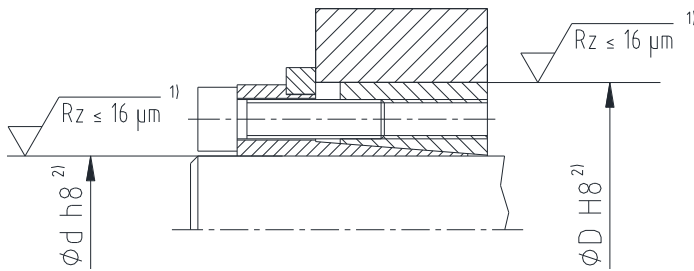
Tolérances et surfaces (exemple : CLAMPEX® KTR 201)
